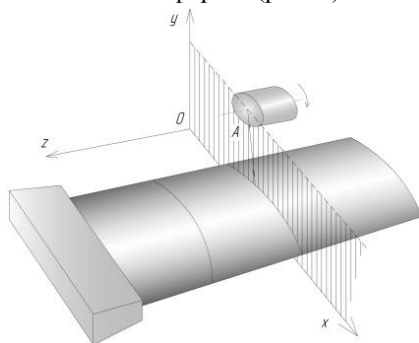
Аксонометрический вид пёра лопатки со стороны спинки с вращающейся оптической насадкой
